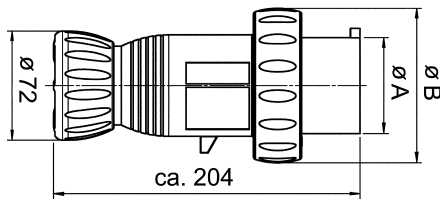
Maßzeichnung Typ 7571/12-506
